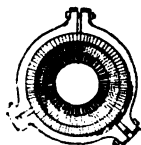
Anneau d'assemblage pour le montage du collecteur.
